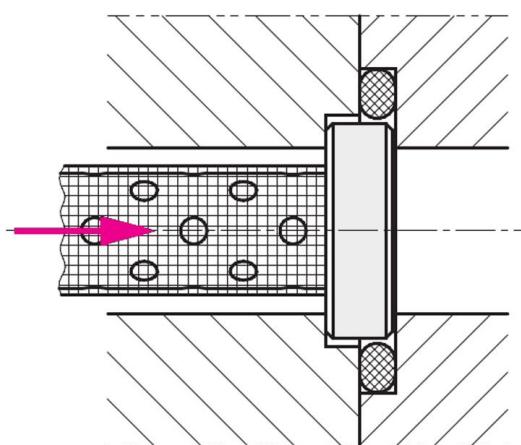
Einbaubeispiel Einsteckfilter 3887066
